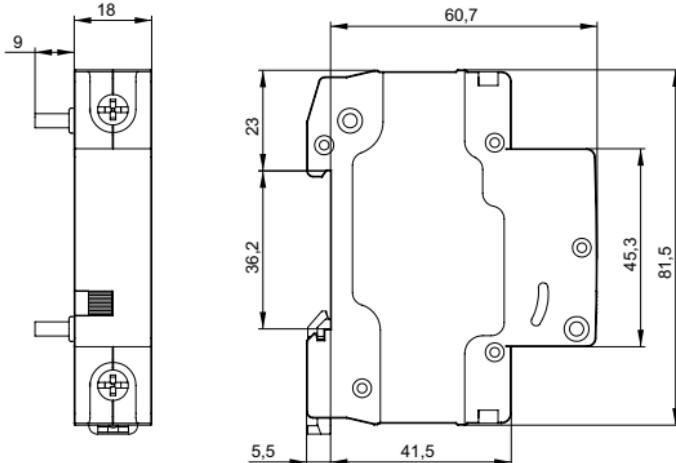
Габаритные размеры PH47 / Figure 1 –Overall dimensions of RN47
